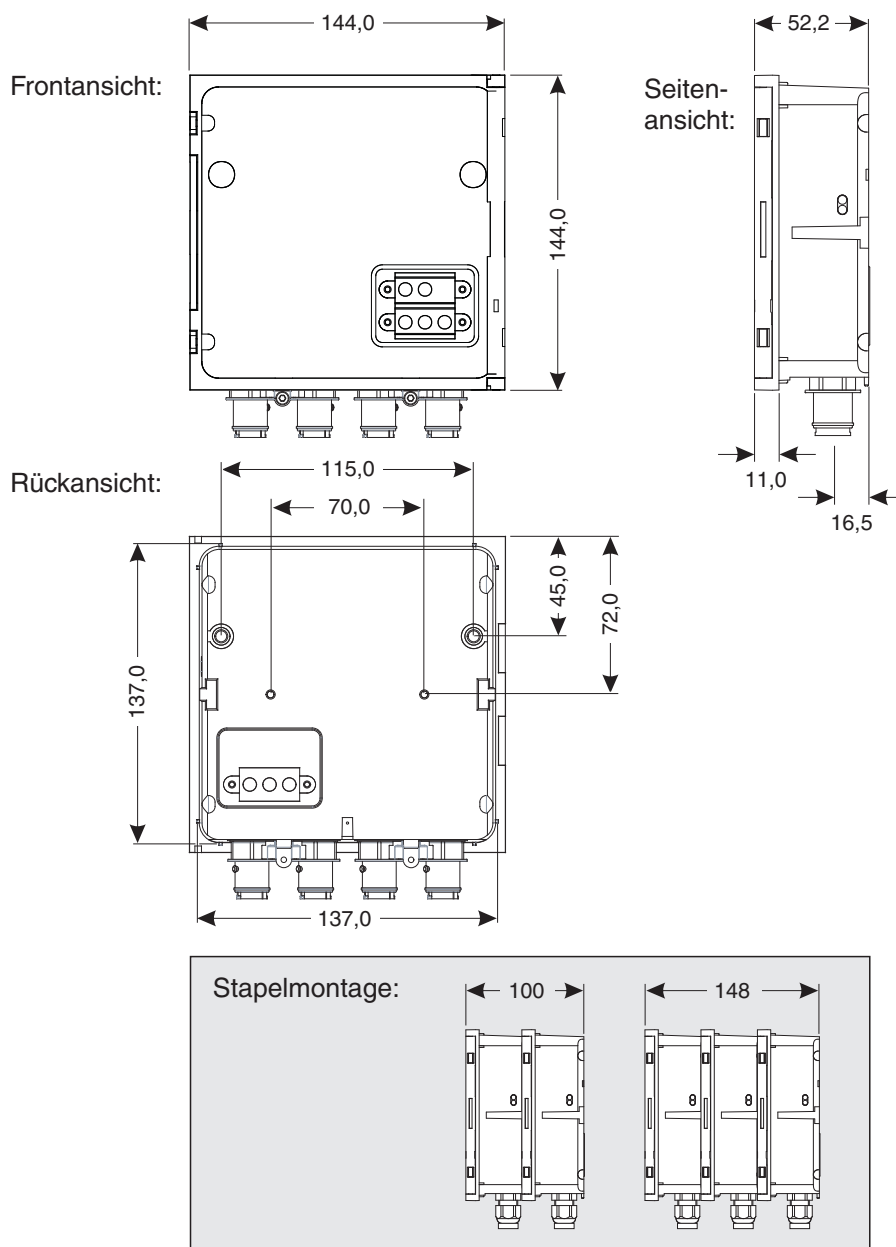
Maßzeichnung MIQ Modul (Maße in mm)
